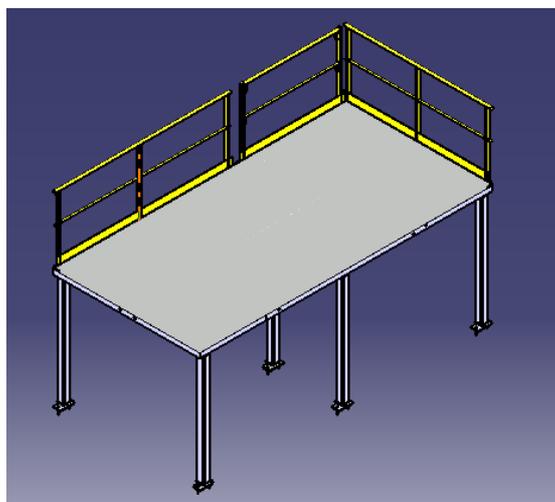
Paso 2 de cada módulo de la plataforma soldada.
